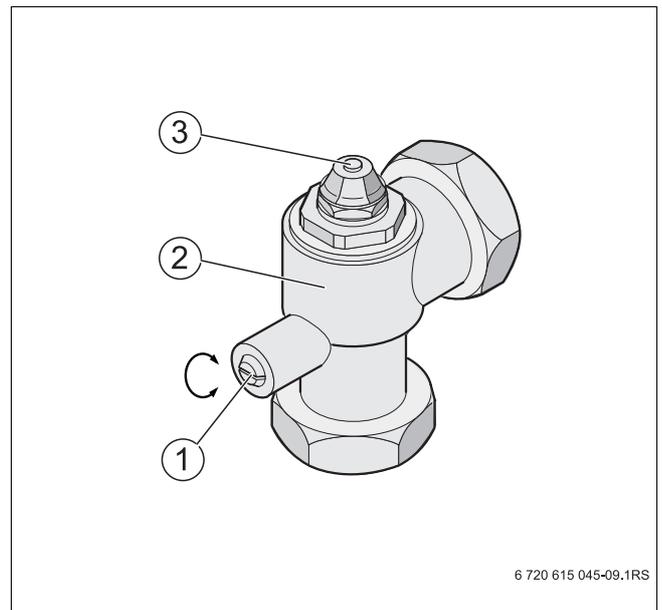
Eck-Rückschlagventil mit Entlüftungsventil
